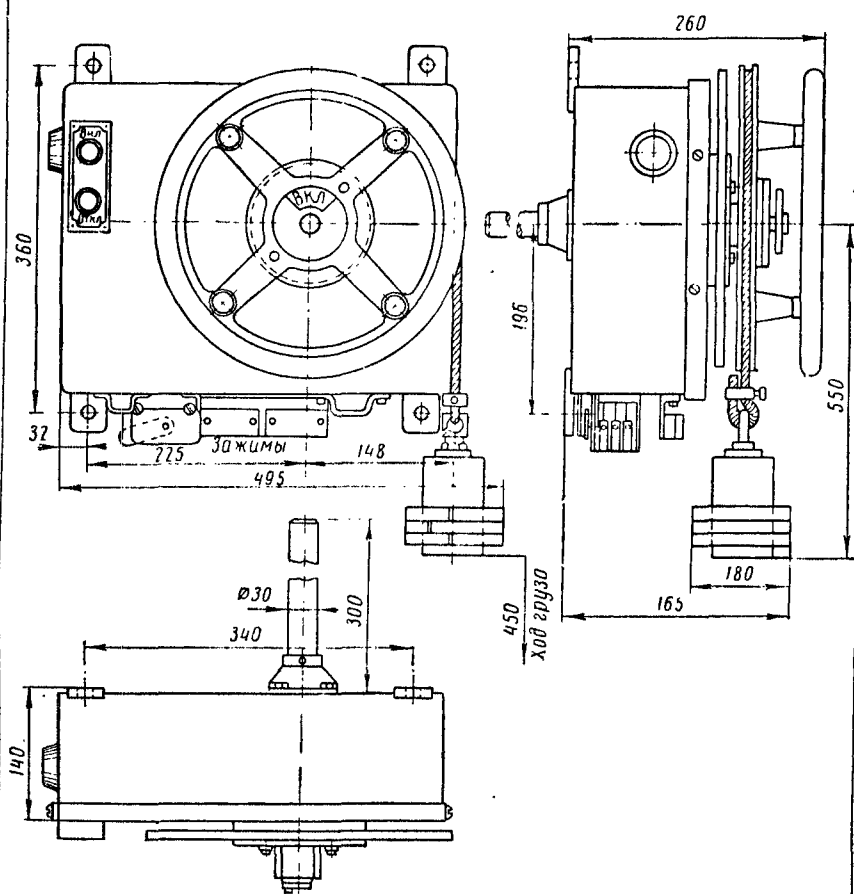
Внешний вид и габаритные размеры грузового привода УГП-51
